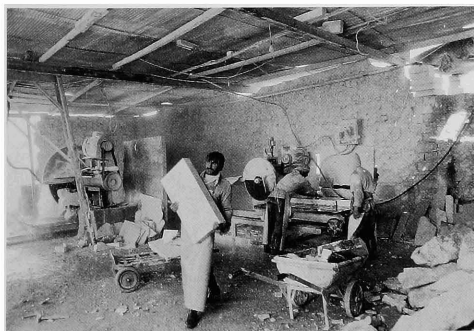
Scierie de la banlieue d'Alep où sont débitées mécaniquement des dalles pour le bâtiment mais aussi parfois des stèles pour les tailleurs de pierre funéraires de la ville.
